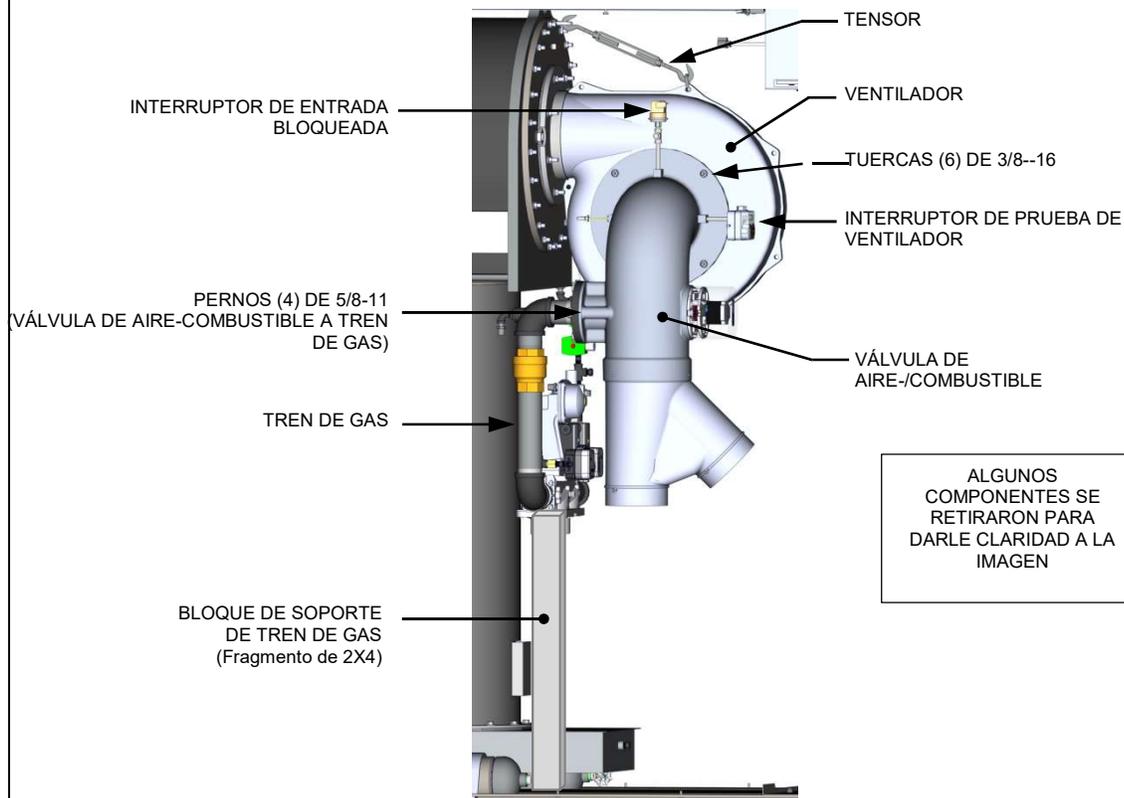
Detalles del montaje de ensamblado del quemador - Vista frontal izquierda
